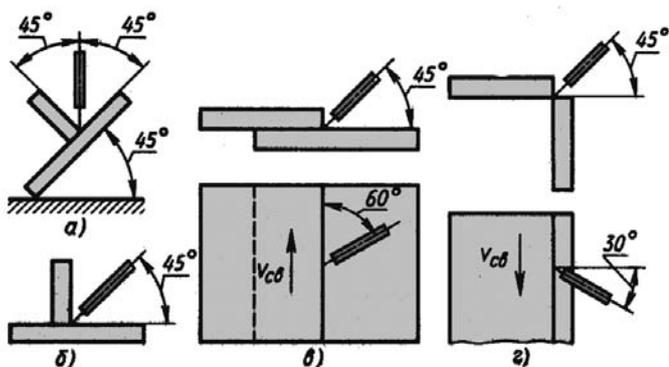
Положение электрода и изделия при сварке; а – в лодочку; б – таврового соединения; в – внахлестку; г – углового соединения
